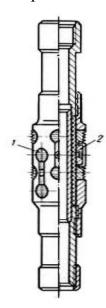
Якорь плашечный гидравлический для ГРП: 1 - плашки с насечками; 2 - резиновый цилиндр
